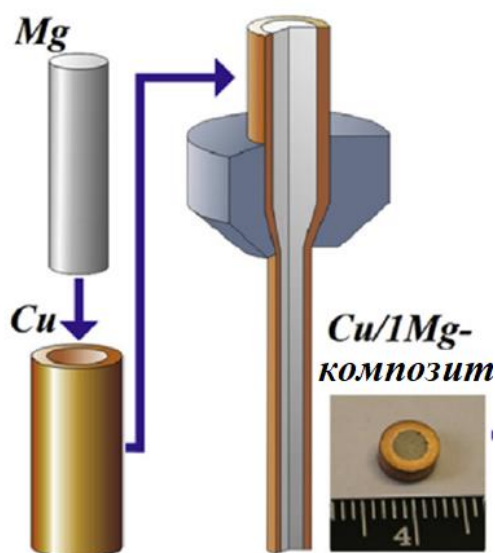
Схема, показывающая этапы получения Cu/1Mg-композита: формирование биметаллической сборки и ее гидроэкструзия через матрицу; справа приведена фотография поперечного сечения композитного прутка Ø6 мм
